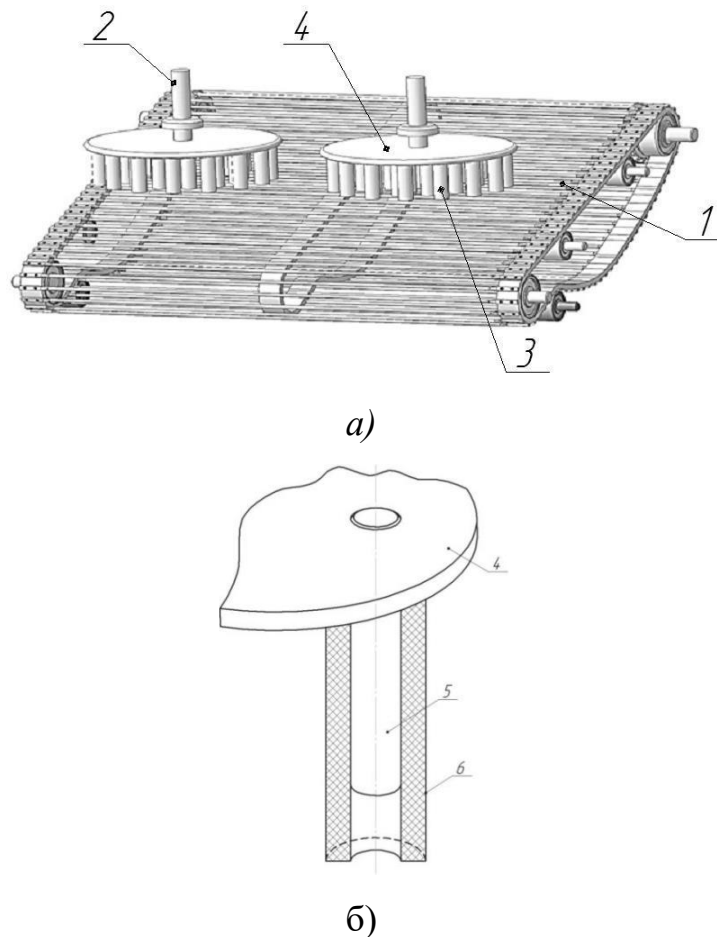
Сепаруючий елеватор із дисковими зворушувачами: а) вигляд загальний, б) робочий елемент (палець) дискового зворушувача: 1 – сепарувальний елеватор, 2 – дисковий зворушувач; 3 – палець; 4 – прогумований диск; 5 – металевий стрижень; 6 – полімерна трубка.
